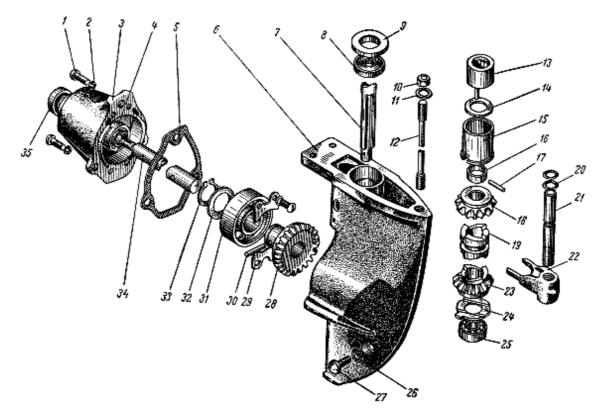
Деталировка редуктора мотора "Москва" в аксонометрии.
